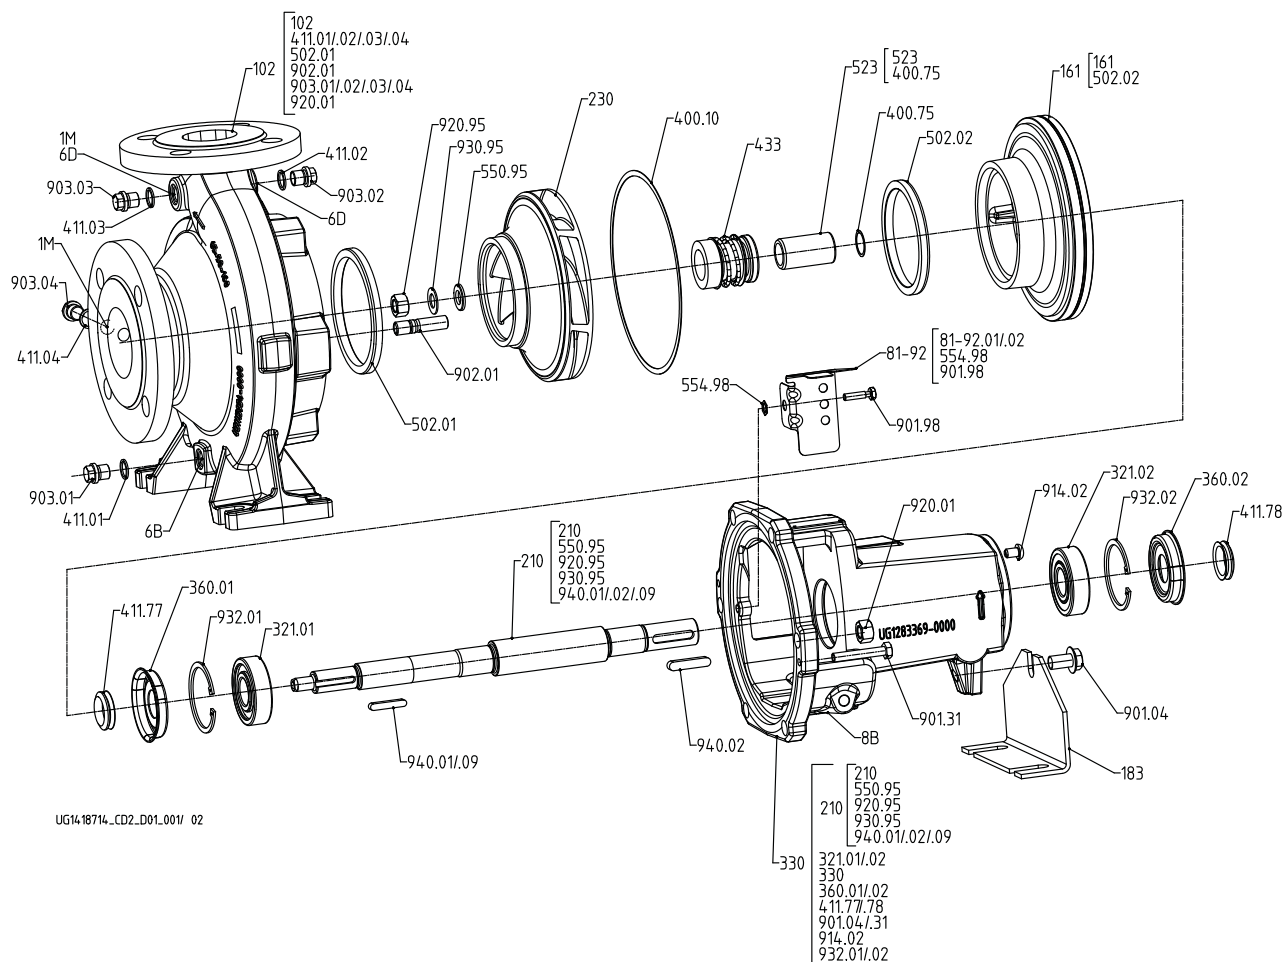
Ausführung mit Normgleitringdichtung und geklemmtem Gehäusedeckel
